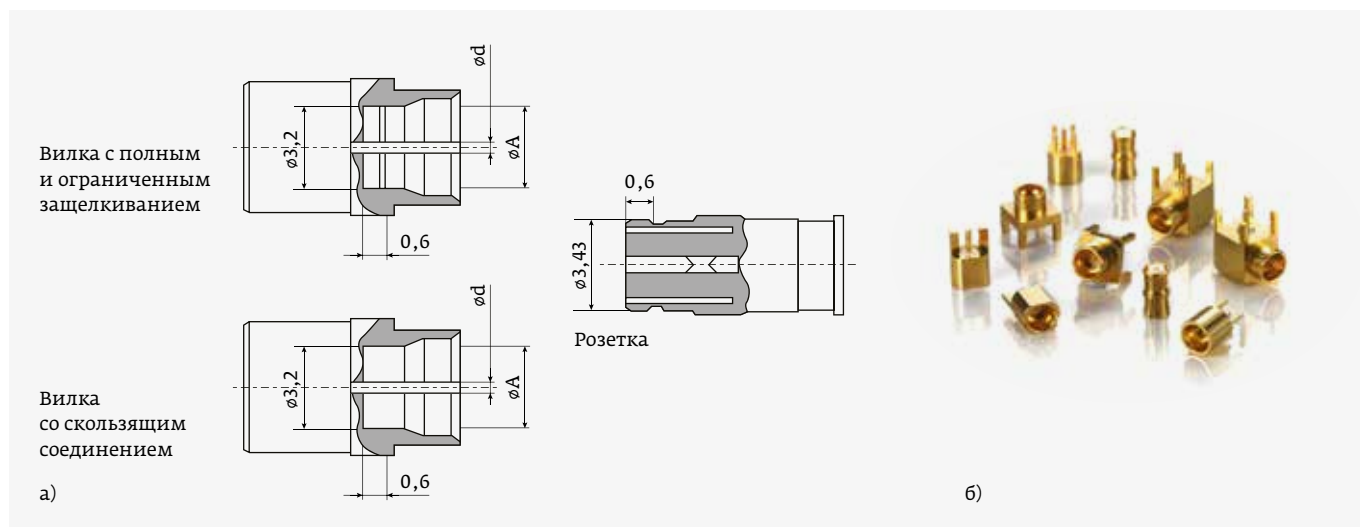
Соединитель SMP: а – конструкция розетки и вилок; б – внешний вид соединителя
